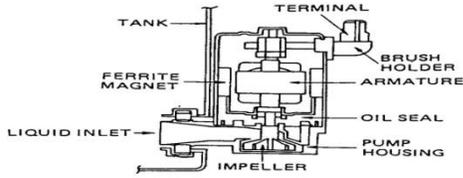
Estrutura esquemática do conjunto motor acoplado à bomba.
